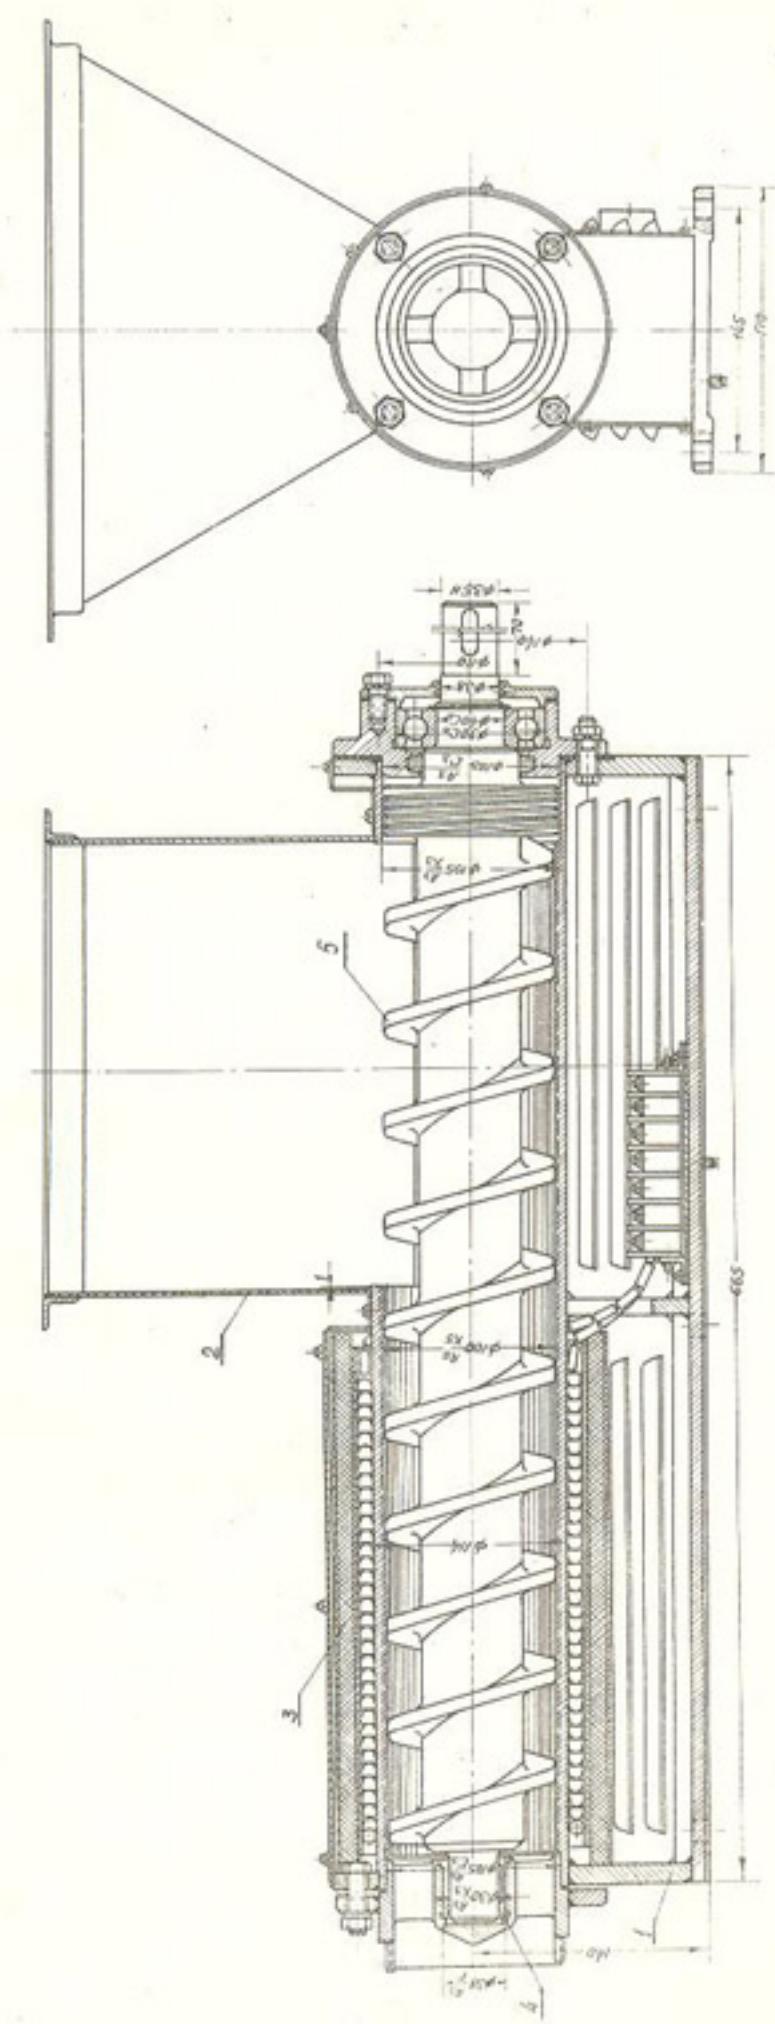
Шнек-пресс для набивки мастики в шприцы: 1-корпус; 2-воронка; 3-нагреватель; 4-головка; 5-шнек
